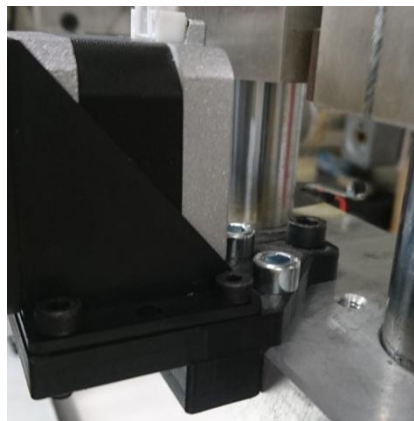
Amarre del soporte extrusor junto con el extrusor al carro de la máquina.
